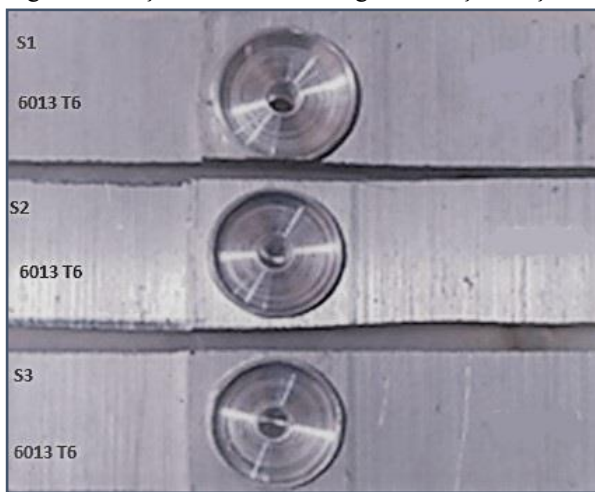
Kaynaklı numunelerin şematik görüntüsü (Schematic view of welded samples).
